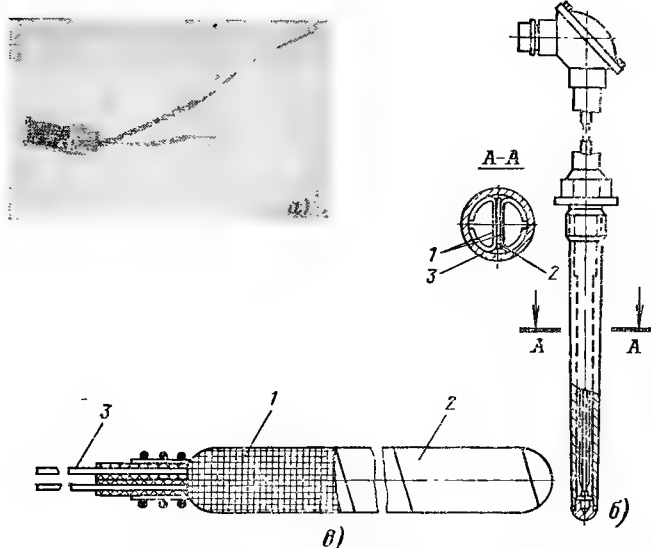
Малоинерционный термометр сопротивления. а — бескаркасный плоский конструкции ОРГРЭС; б — заводского изготовления: 1 — упругие лепестки; 2 — чувствительный элемент; 3 — защитный чехол; в — бескаркасный с безындукционной намоткой: 1 — намотки из медной проволоки; 2 — фторопластовая пленка; 3 — выводы.
